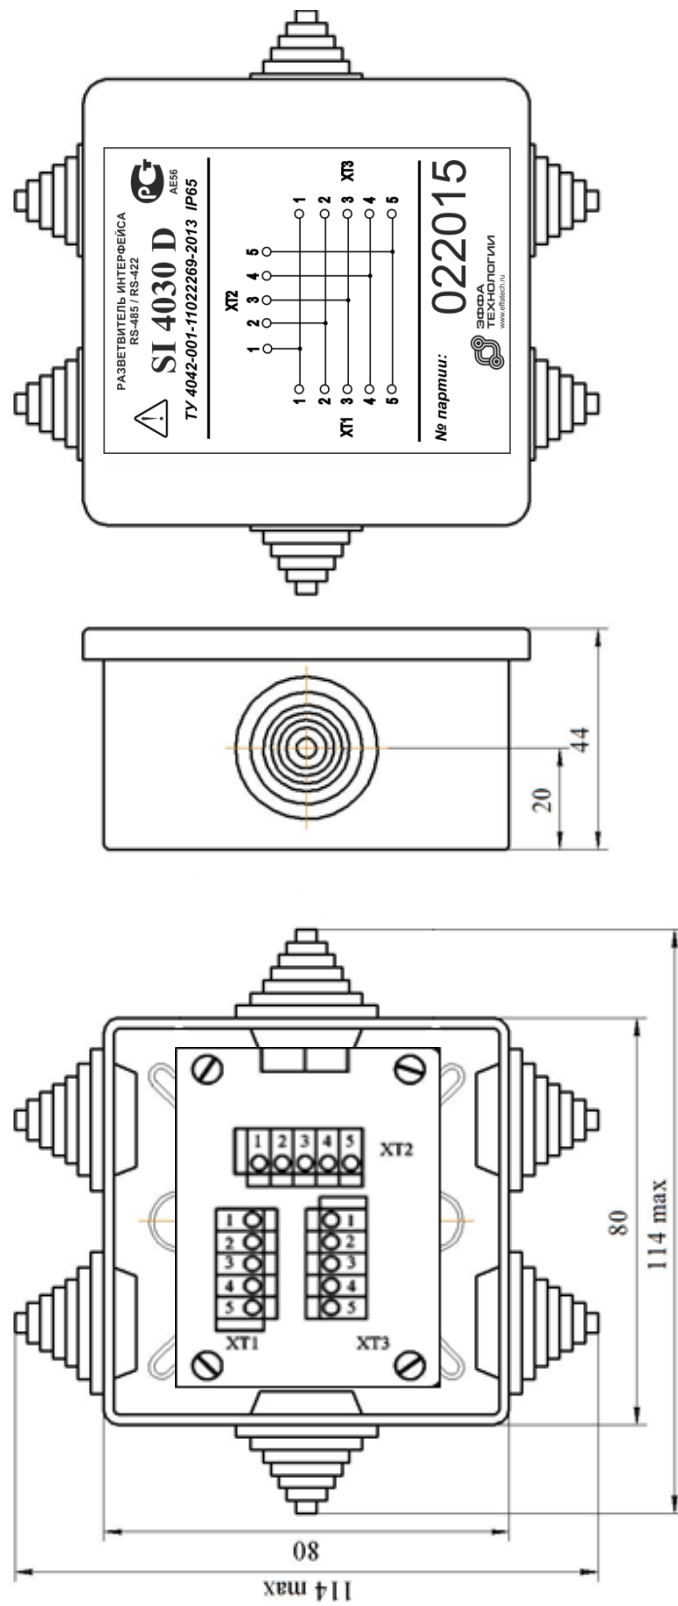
Габаритные и установочные размеры разветвителя SI 4030D
